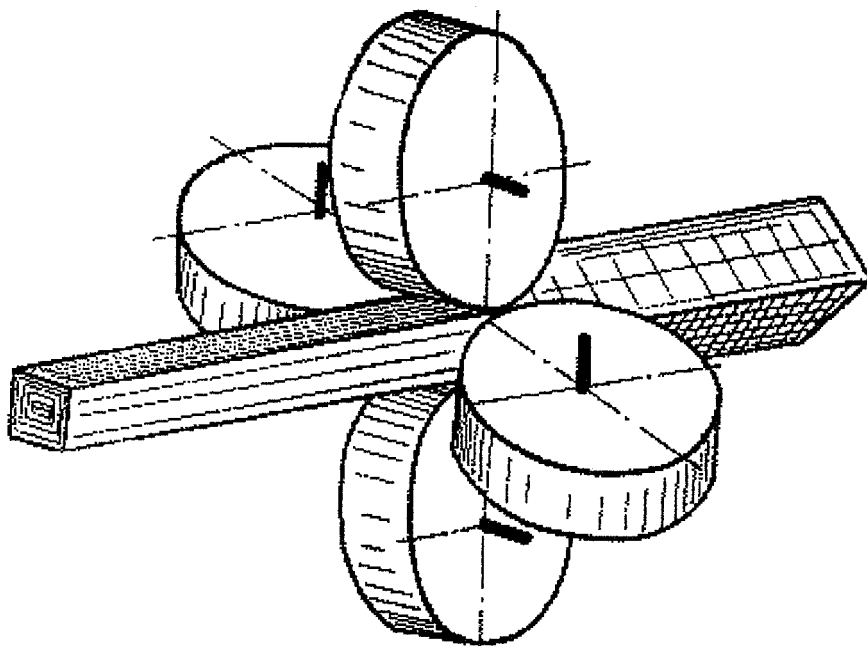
Схема прокатки квадратной полосы в четырехвалковом калибре
